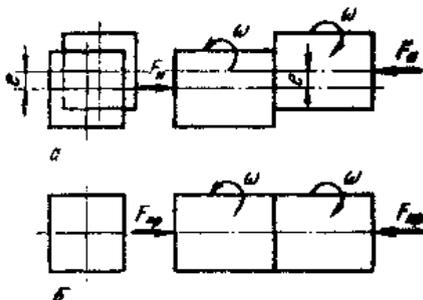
Схема орбитальной сварки трением:
